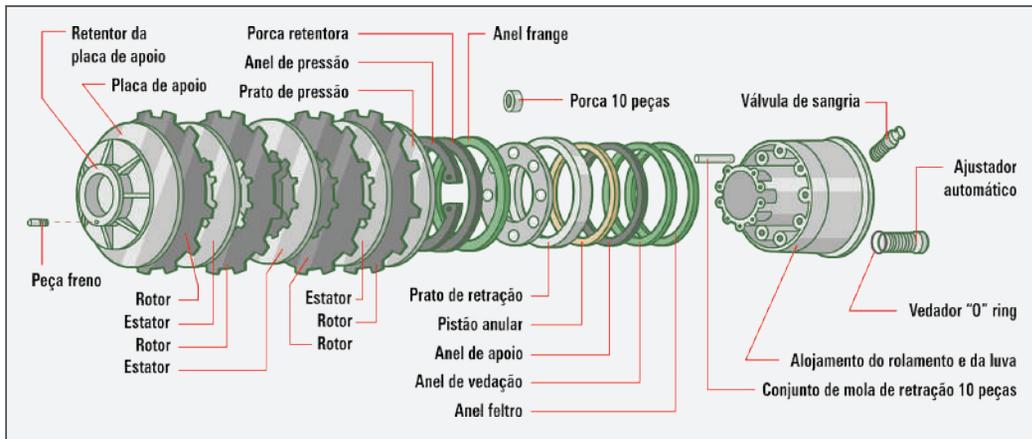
Vista explodida de um conjunto de freios de múltiplos discos
